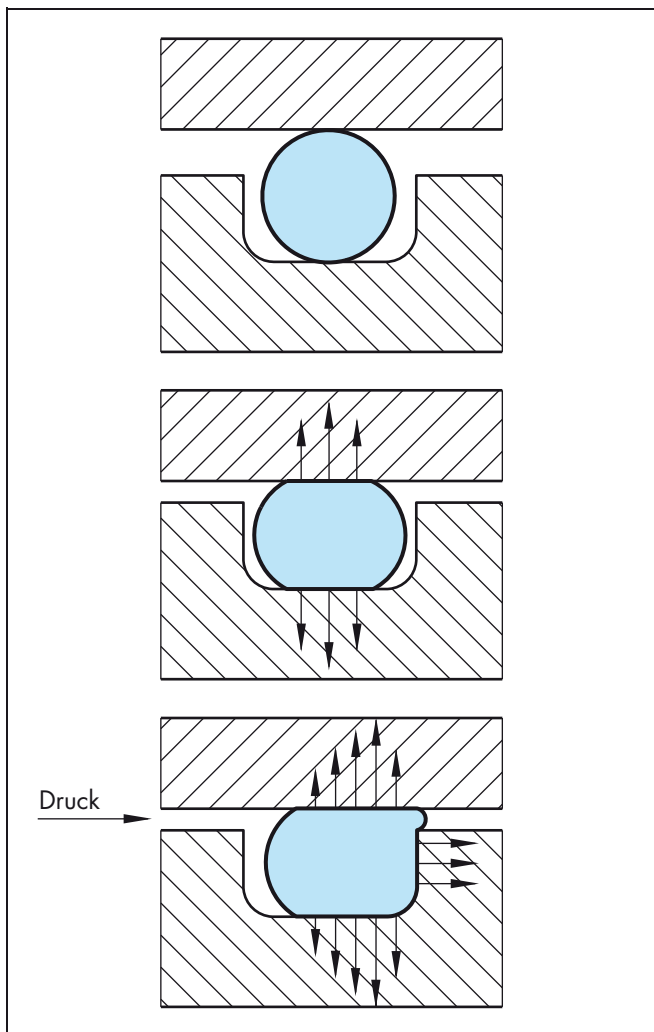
O-Ring Anpresskräfte mit und ohne Systemdruck
